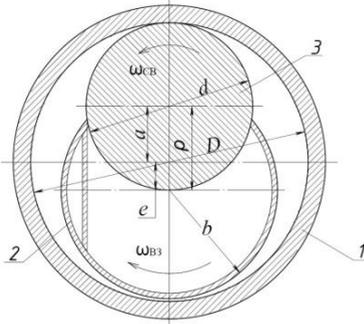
Конструктивная схема вибровозбудителя: 1 – корпус вибровозбудителя; 2 – ведущее звено; 3 – бегунок
